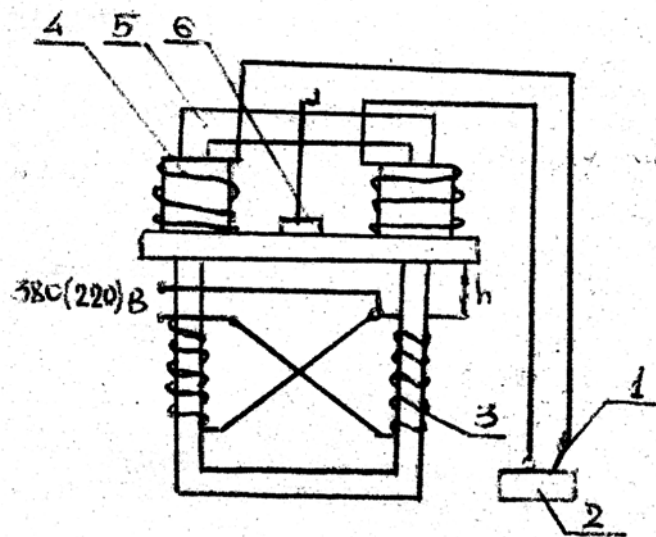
Схема зварювального трансформатора ТД-500:
